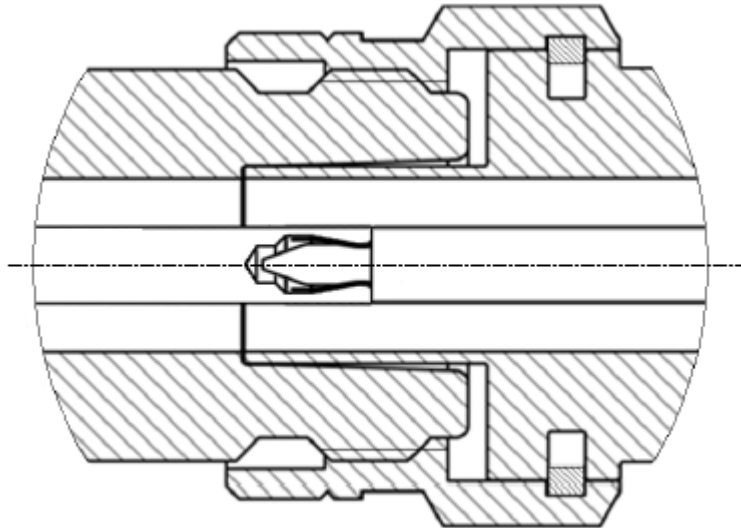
Соединители тип N (розетка слева, вилка справа)
